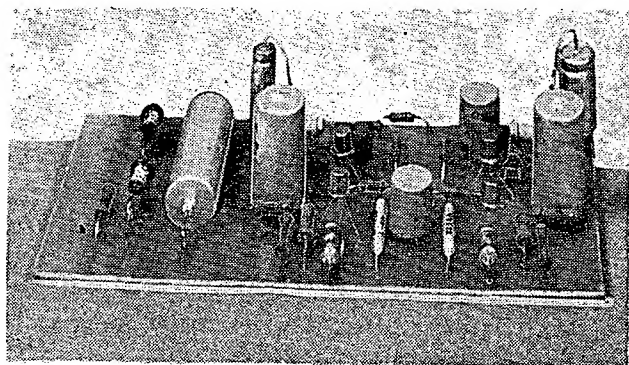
Deska s plošnými spoji předzesilovače (Smaragd D80)
